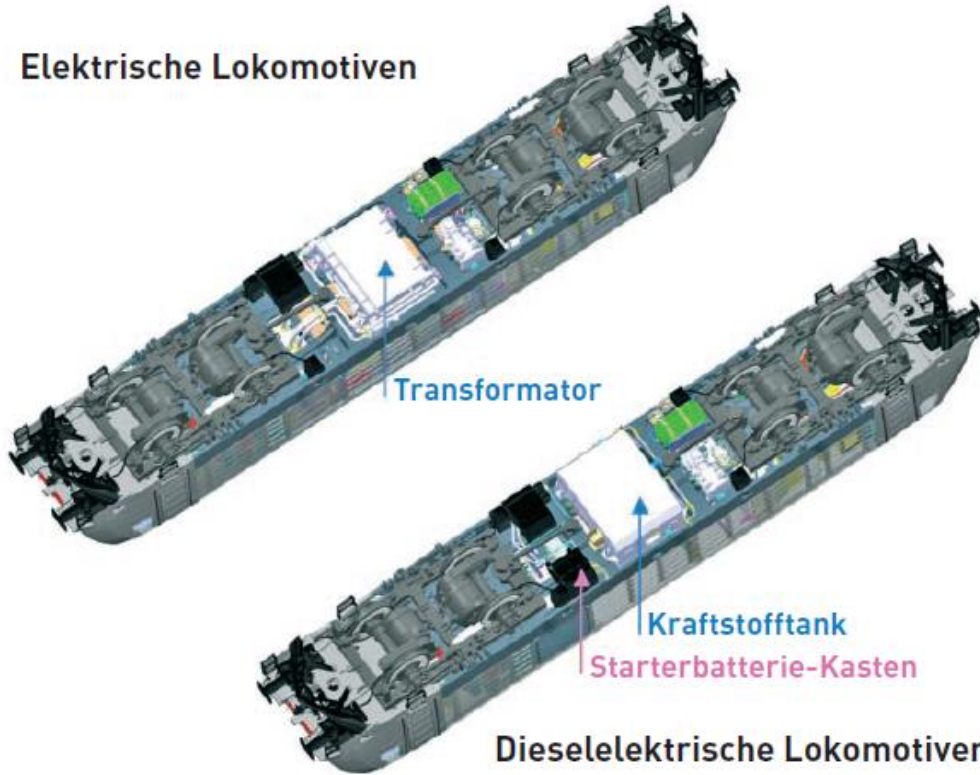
Befestigung des E- oder D – Power-Package auf dem Mittellangträger [13]
